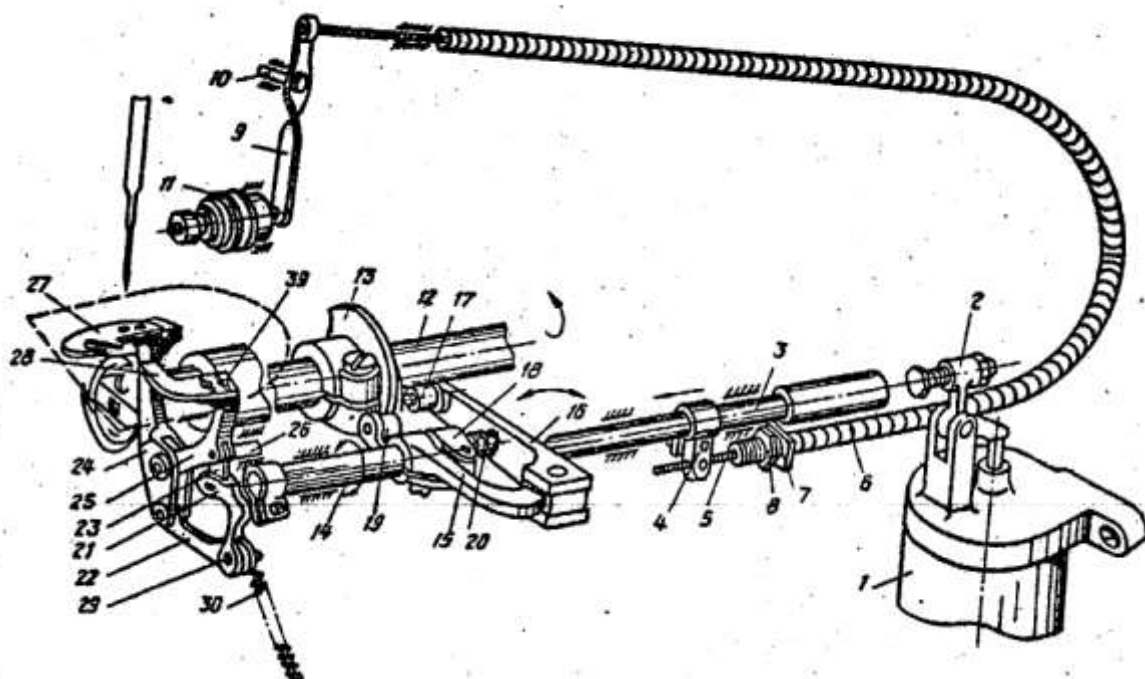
Механізм обрізки ниток, вид аксонометрії
